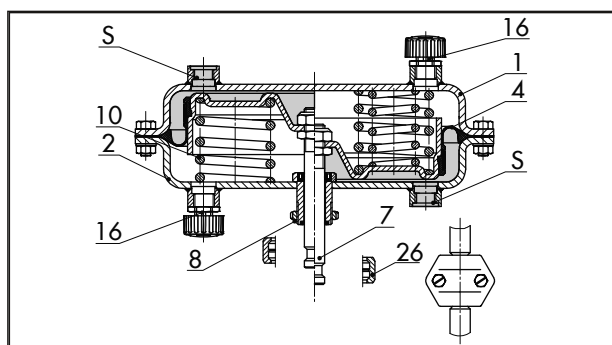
Tipo 3271 · Lado derecho con resortes adicionales
